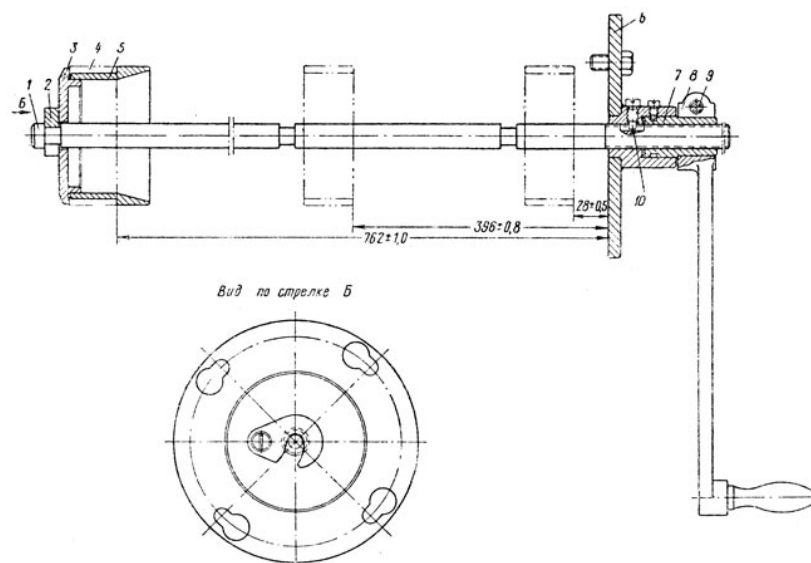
Пристосування для випресовки втулкових підшипників двигунів:
